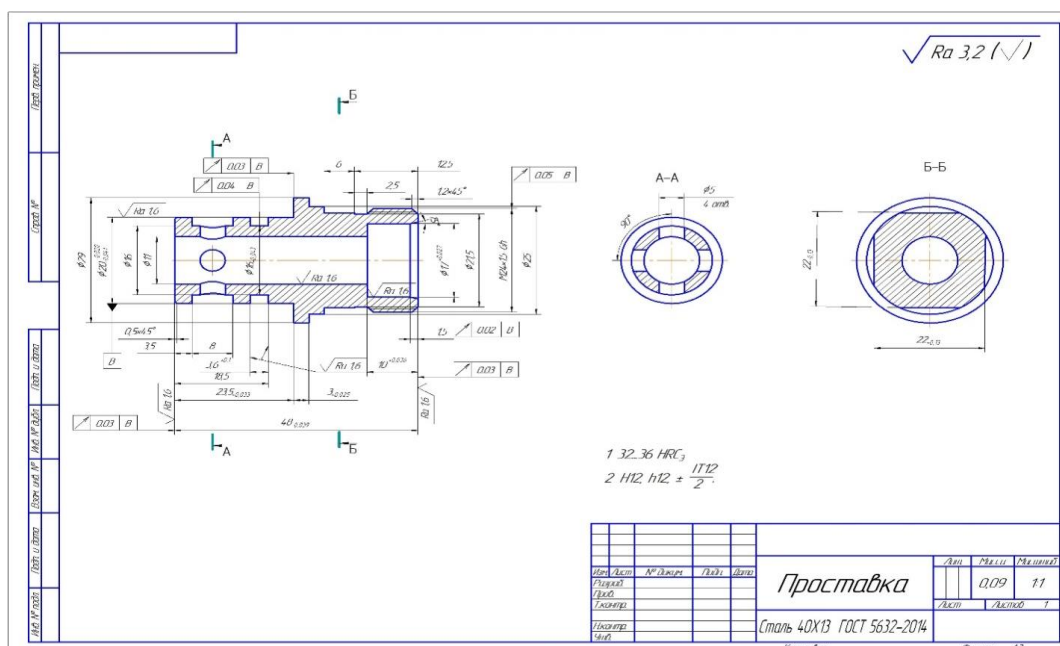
Исходный эскиз детали «Проставка»
